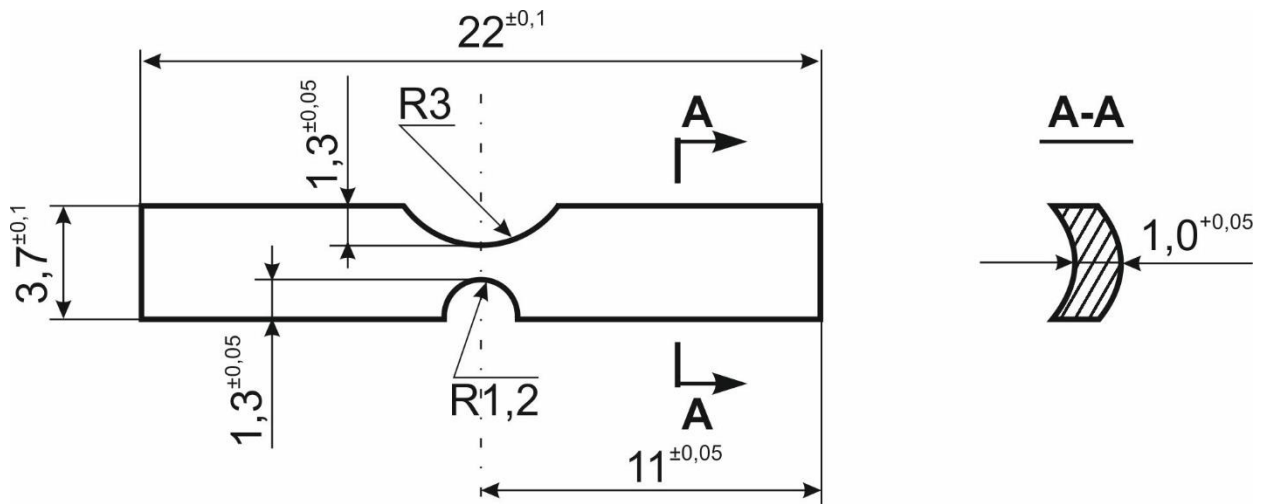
Образец для испытаний на ударный изгиб, изготовленный из испытанного образца для автоклавных испытаний на рисунке 2.5
